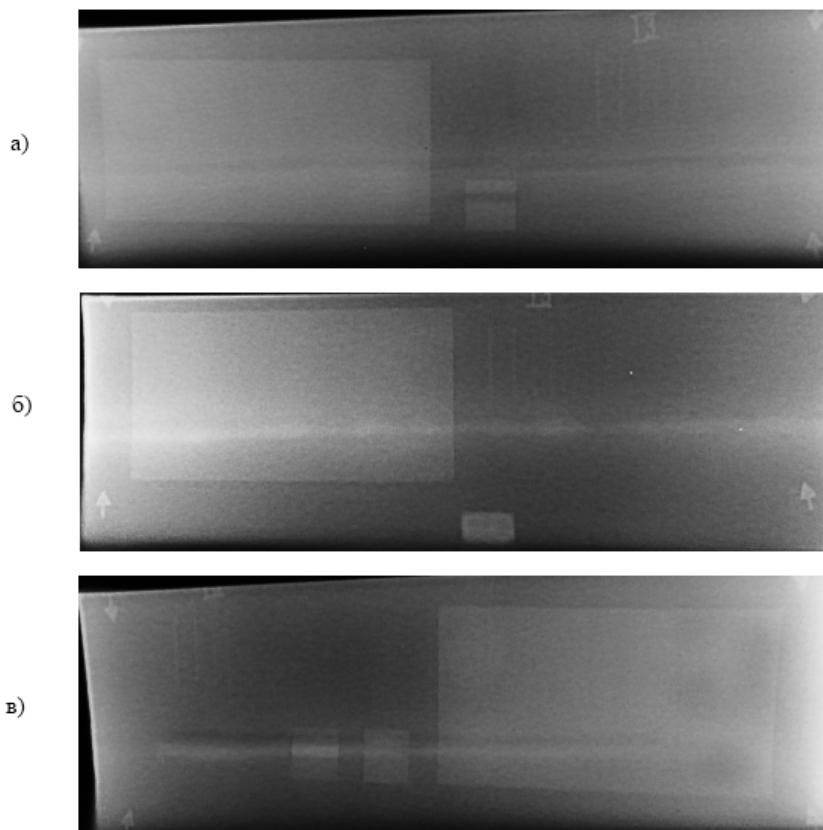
Изображение контролируемого участка на пленке (повторный контроль): а) утяжка сварного шва; б) проплав сварного шва; в) утяжка и проплав (при равной величине h_3 имитаторов)
